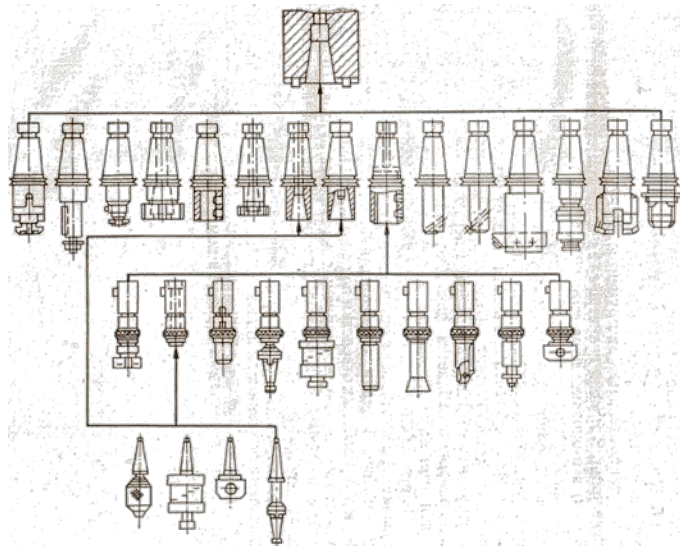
Підсистема допоміжного інструменту для БВ свердлильно-фрезерно-розточувальної групи
